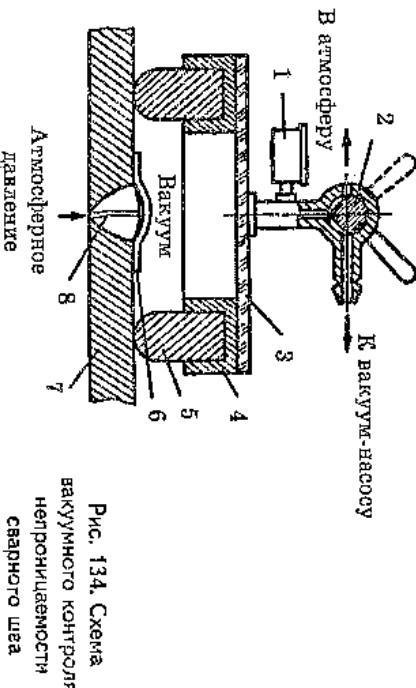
Схема вакуумного контроля непроницаемости сварного шва
